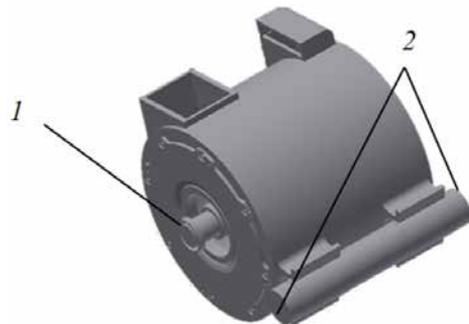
Твердотельная модель колесно-моторный блок электровоза
